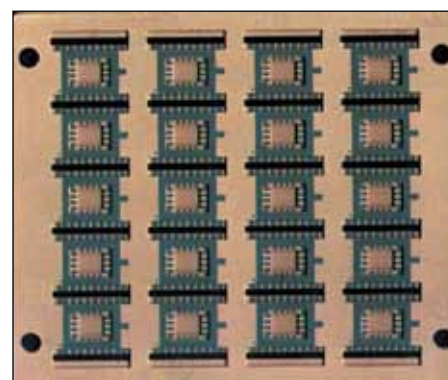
Пакет из трех карт с отверстиями — групповая заготовка для корпусов «ТИР» (предприятие «ДЗРД»)
